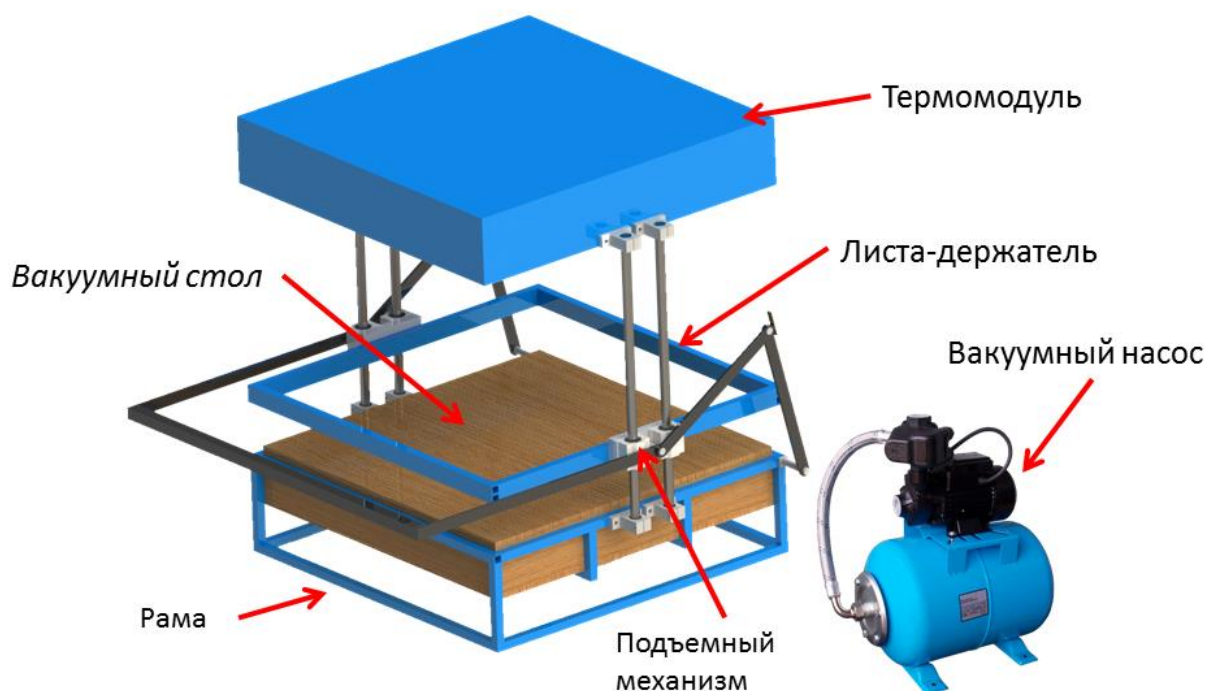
Конструкция разрабатываемого вакуумно формовочного станка для применения в лабораторных работах. 1) Термомодуль - нагревательный элемент служащий для нагрева пластмассы до пластичности. 2) Вакуумный стол - стол с множеством отверстий диаметром 2-4 мм, через эти отверстия лист притягивается к матрице при помощи вакуума. 3) Листа-держатель - зажимной механизм для листа пластмассы. 4) Подъемный механизм - предназначен для перемещения листа-держателя с листом пластмассы, между термомодулем и вакуумным столом. 5) Станина - рама, основание станка. 6) Вакуумная станция - предназначена для нагнетания вакуума.
